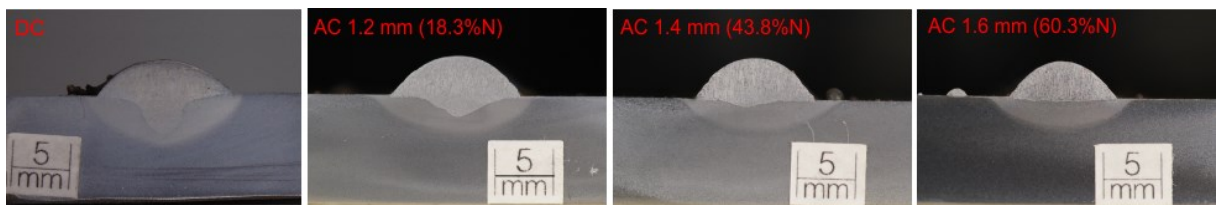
Macrografia de soldagem sobre chapa para processo GMAW-P DC e GMAW-P AC com diâmetro de gota de 1.2, 1.4 e 1.6 mm.
